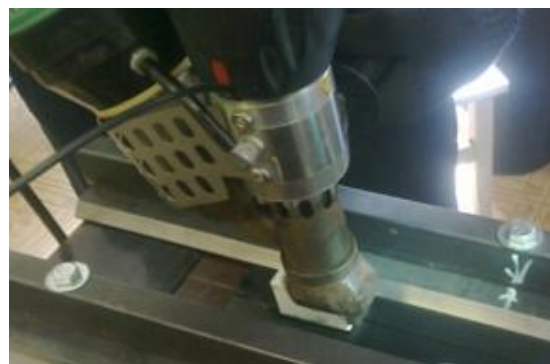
Экструзионная сварка КСС стыковых соединений СЗ
